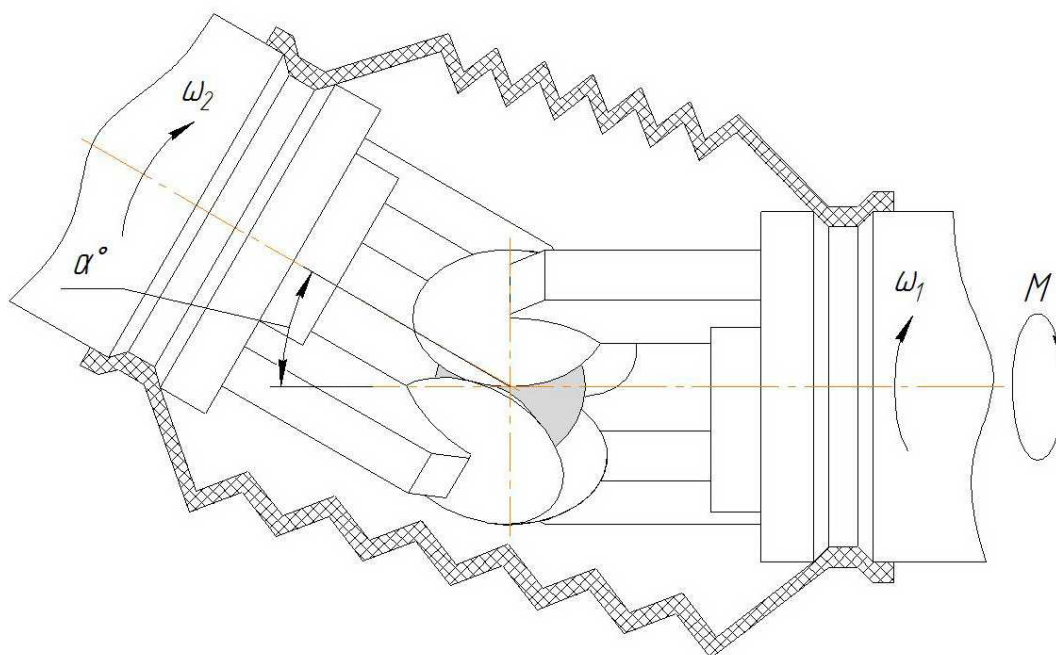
Процесс передачи вращающего момента M с ведущего вала на ведомый под углом α° к общей продольной оси шарнира
